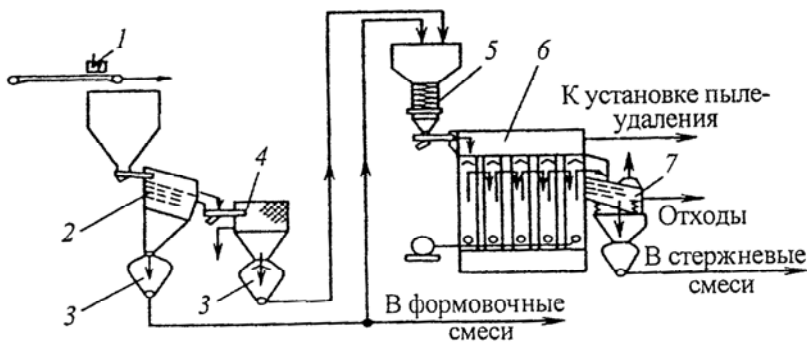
Схема пневматической регенерационной установки для переработки формовочной и стержневой смесей: 1 – магнитный сепаратор; 2 – грохот; 3 – камерный насос; 4 – шаровая мельница; 5 – охладитель песка; 6 – пневморегенератор; 7 – классификатор
